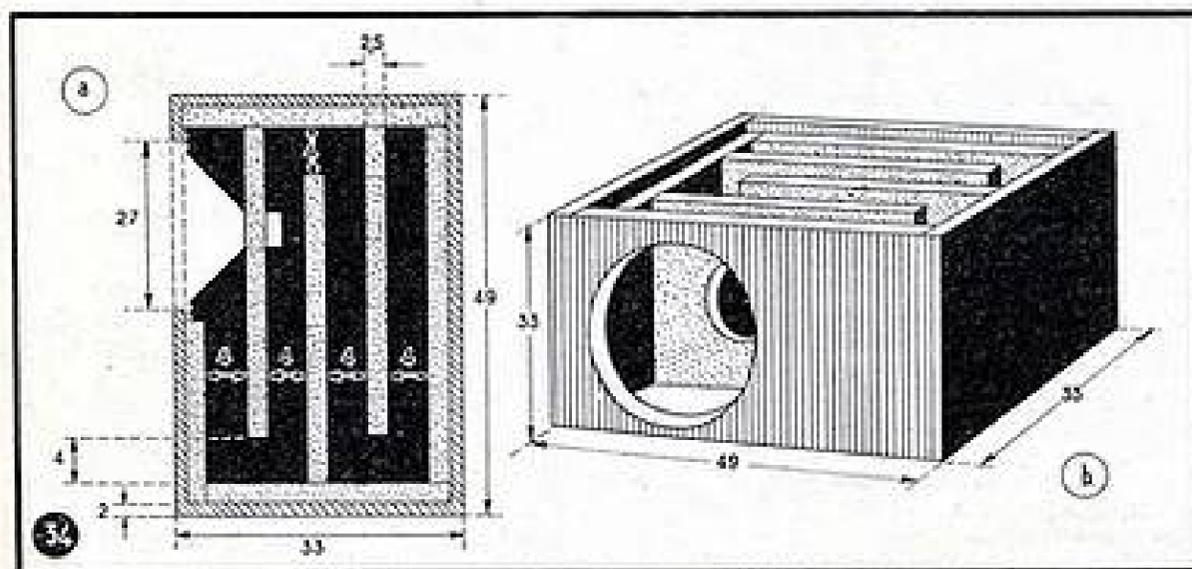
Labyrinthe fermé (d'après R.T.N.) A) : Coupe-élévation (dimensions en cm) ; B) : Vue perspective avant fixation de la face latérale.
